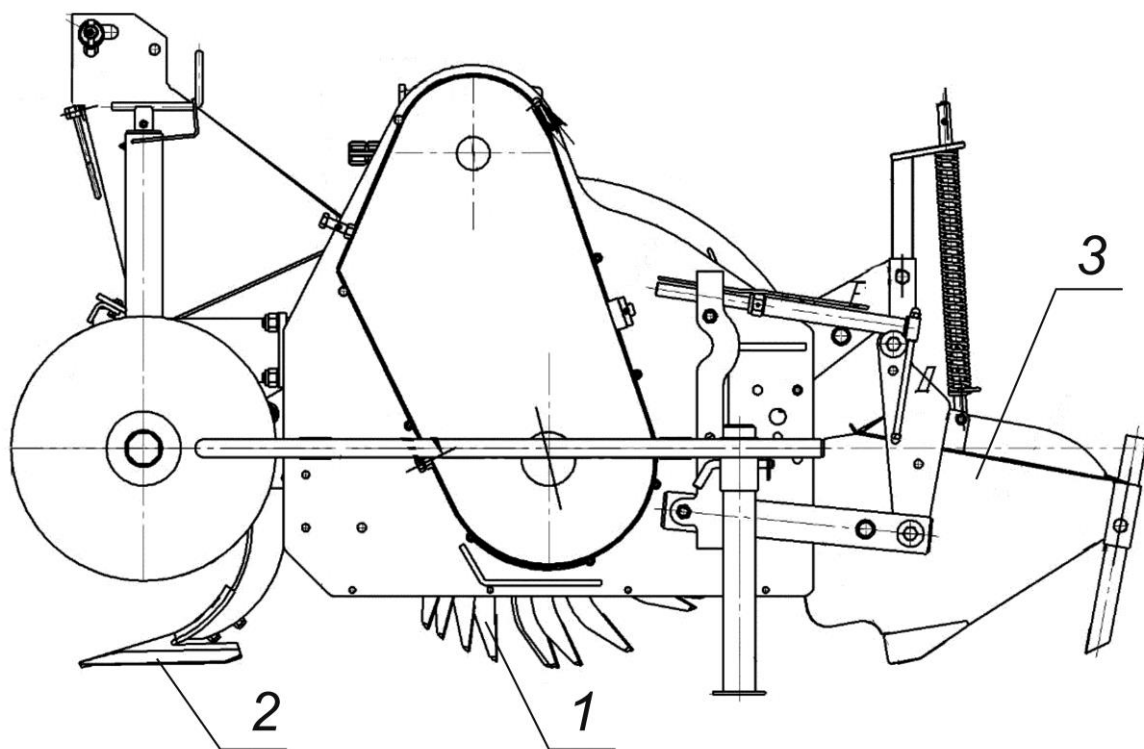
Фрезерный культиватор ГПК-1 для нарезки гребней
